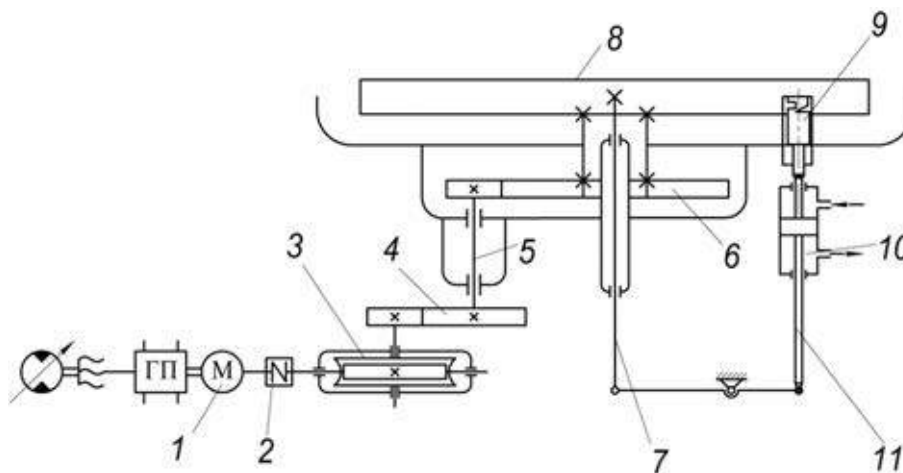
Кінематична схема поворотного столу агрегатного верстата з гідроприводом
